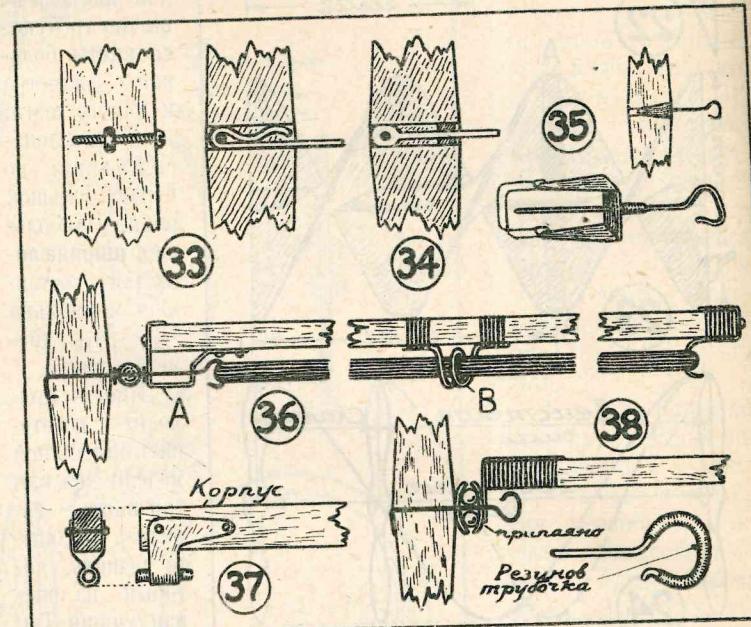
, 34, 35. Различные способы укрепления воздушного винта на валу резинового двигателя. Рис. 36, 37 и 38. Различные типы подшипников для вала.
